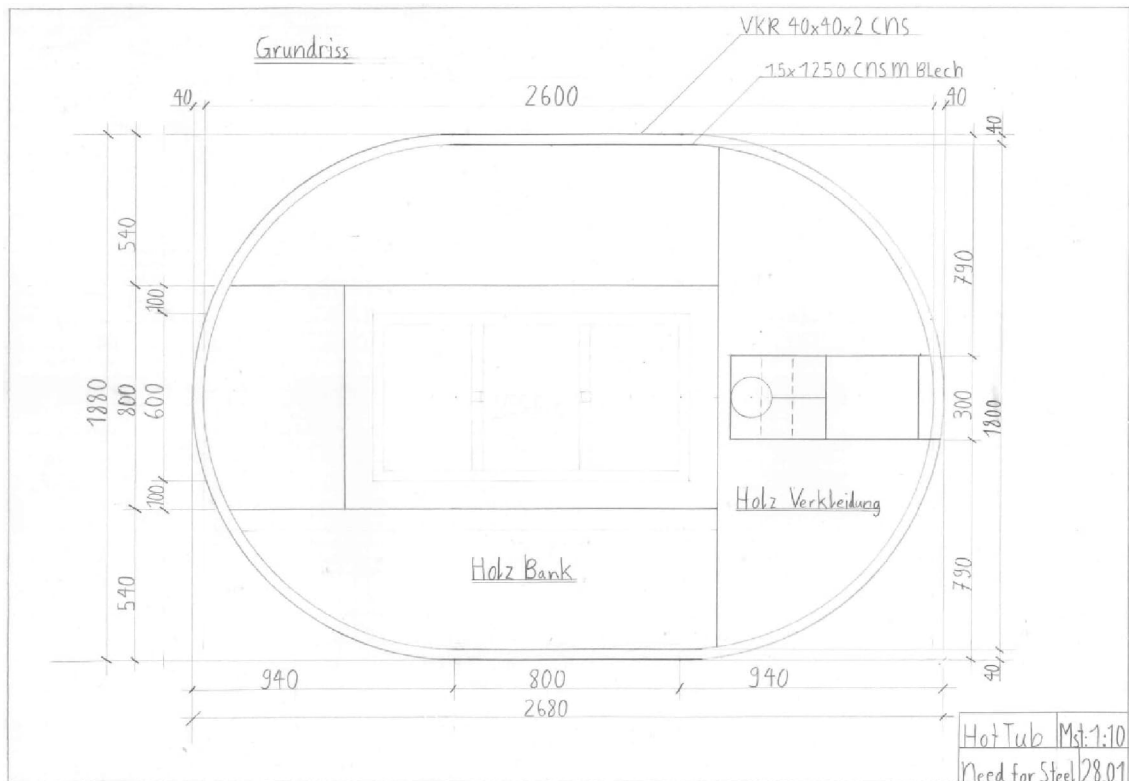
Plan Hot-Tub gerundet, Massstab 1:10
